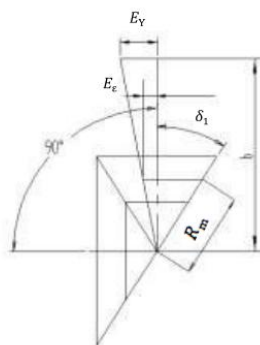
大小锥 齿轮的轴承孔中心线的垂直度公差
